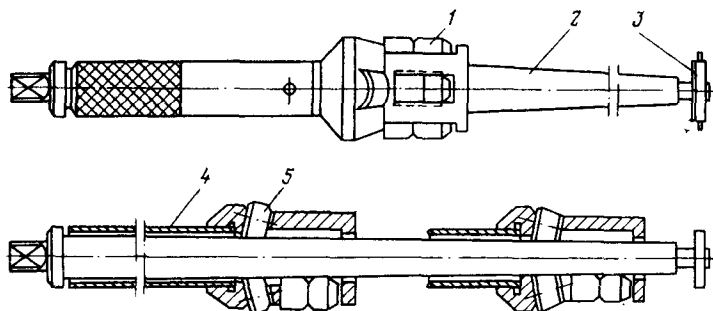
Вальцовка (вверху — общий вид, внизу — разрез):
